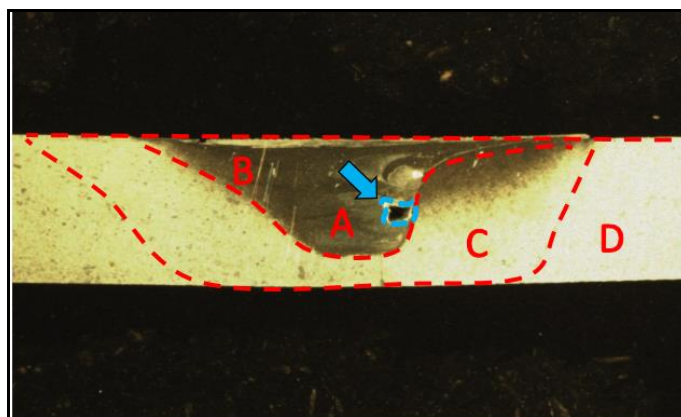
Macrografia da solda realizada com ferramental cônico em AISI H13
